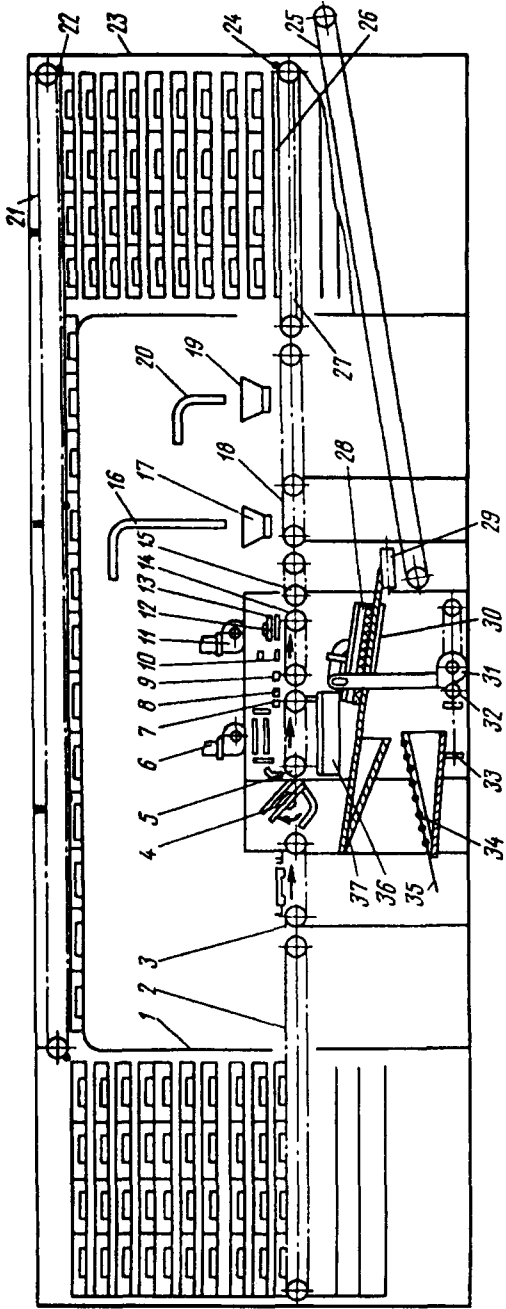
Конфетошливный агрегат с установкой ускоренной выстойки корпусов конфет
